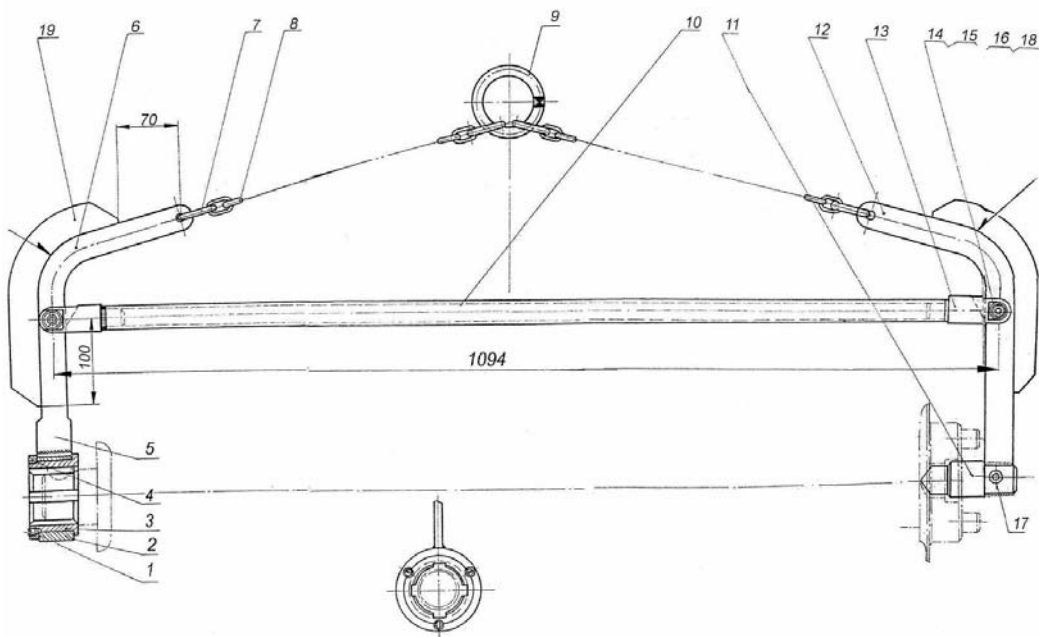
Подвеска для снятия и установки коленчатого вала
